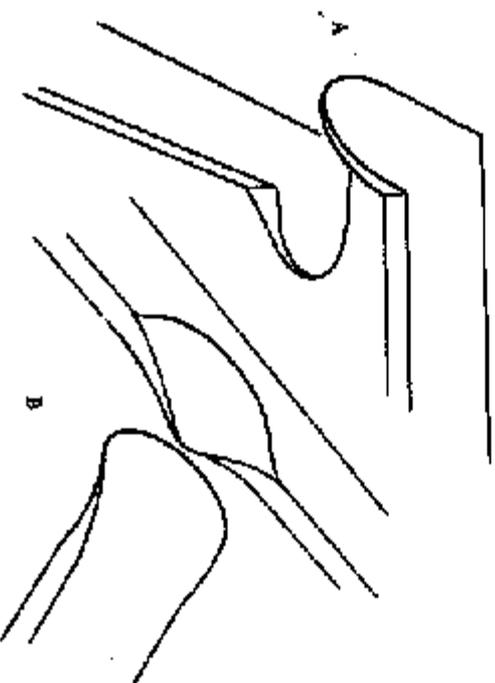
Las uniones en escuadra (A) y en T (B) en estructuras planas, requieren soldaduras especiales.
